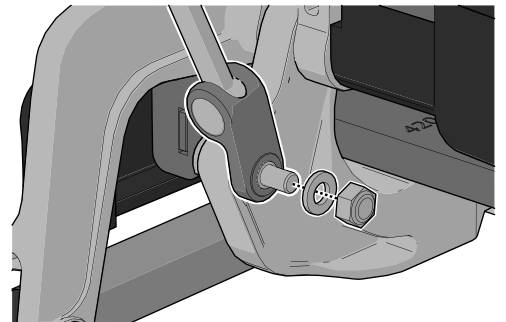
Halten Sie die Gelenkschraube fest, um die Mutter entfernen zu können.
